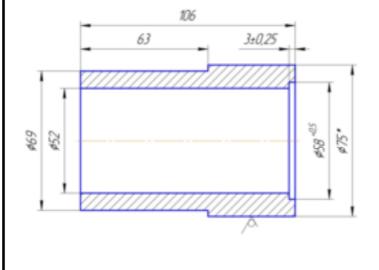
Общий вид заглушки до механической обработки перед сваркой и после сварки в составе оси
